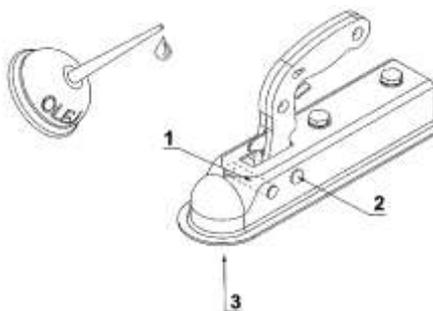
Схема смазки сцепного устройства прицепа П05.02-01
